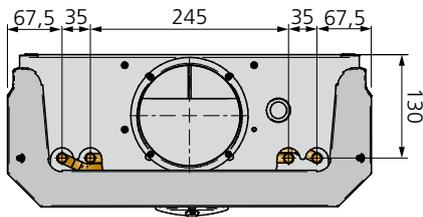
Dimensions WISE Adriatic, vue arrière du raccordement hydraulique
